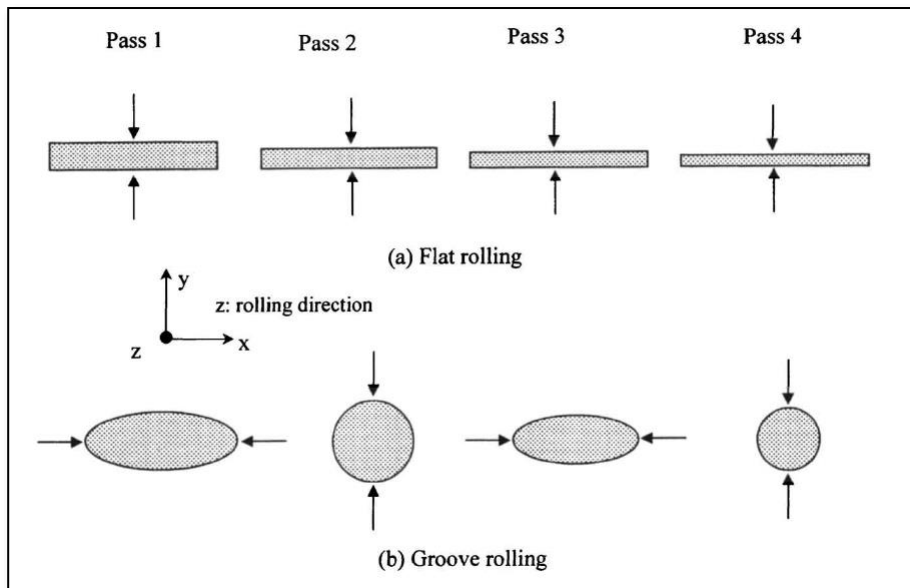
Fuerzas de reducción en la laminación de planos y laminación de barras redondas.
